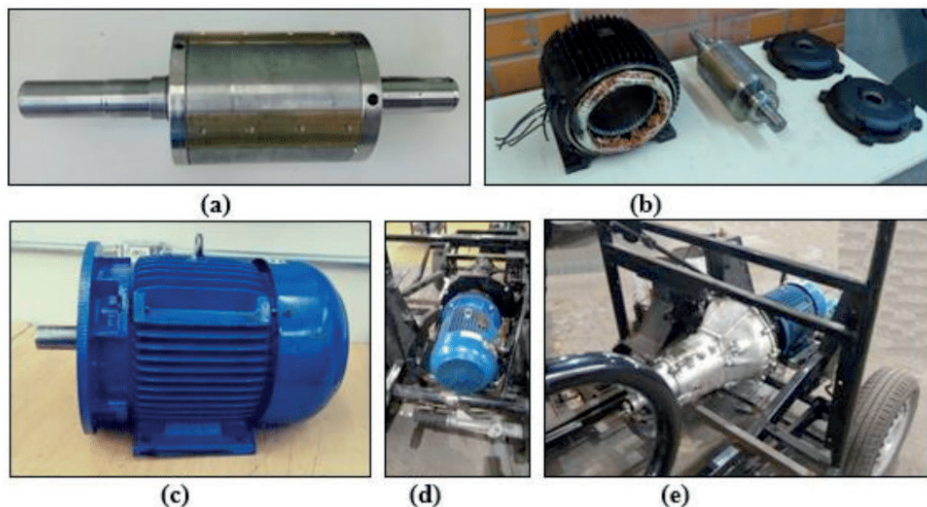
Motor elétrico síncrono trifásico para tração do veículo – (a) Rotor sinterizado – (b) Estator e Tampas – (c) Motor Montado e Pintado – (d) Motor montado no Veículo – (e) Detalhe da Caixa de Câmbio
